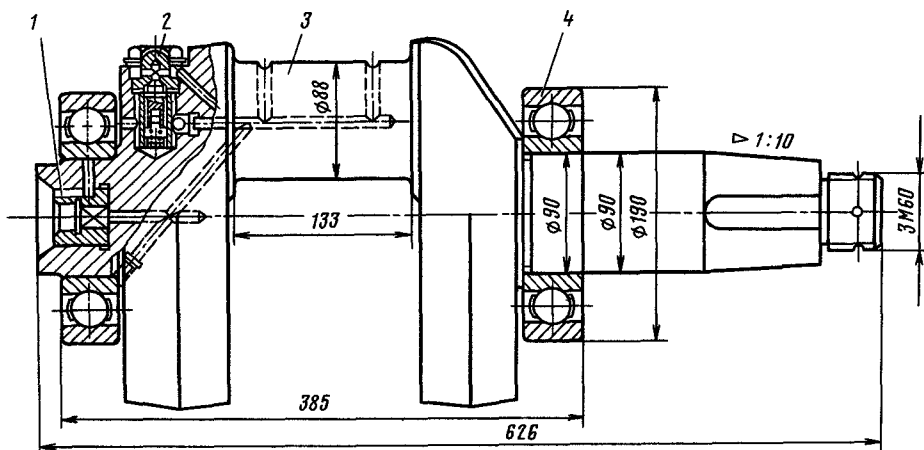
Коленчатый вал компрессора КТ6 в сборе:
